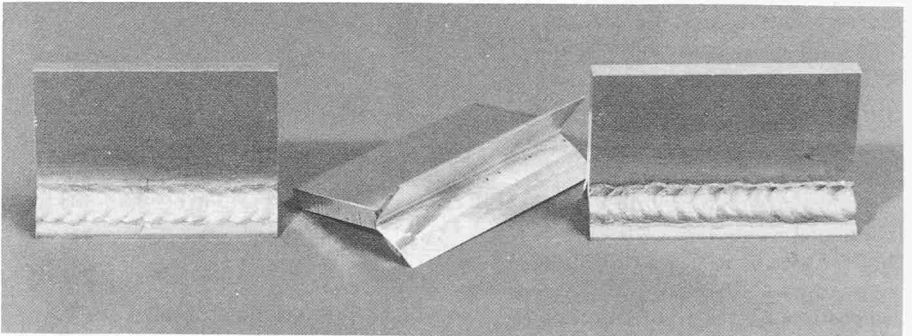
Durch Schichtfräsen freigelegte Poren in Schweissraupen
